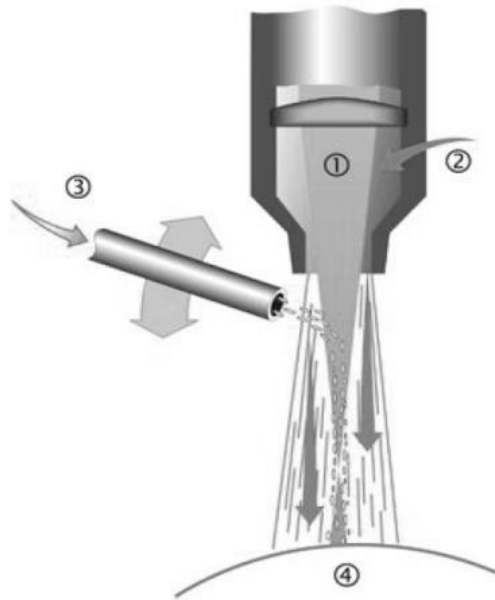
Схема лазерного порошкового наплавлення: 1 – лазерний промінь; 2 – захисний газ; 3 – порошок; 4 – деталь [2].
